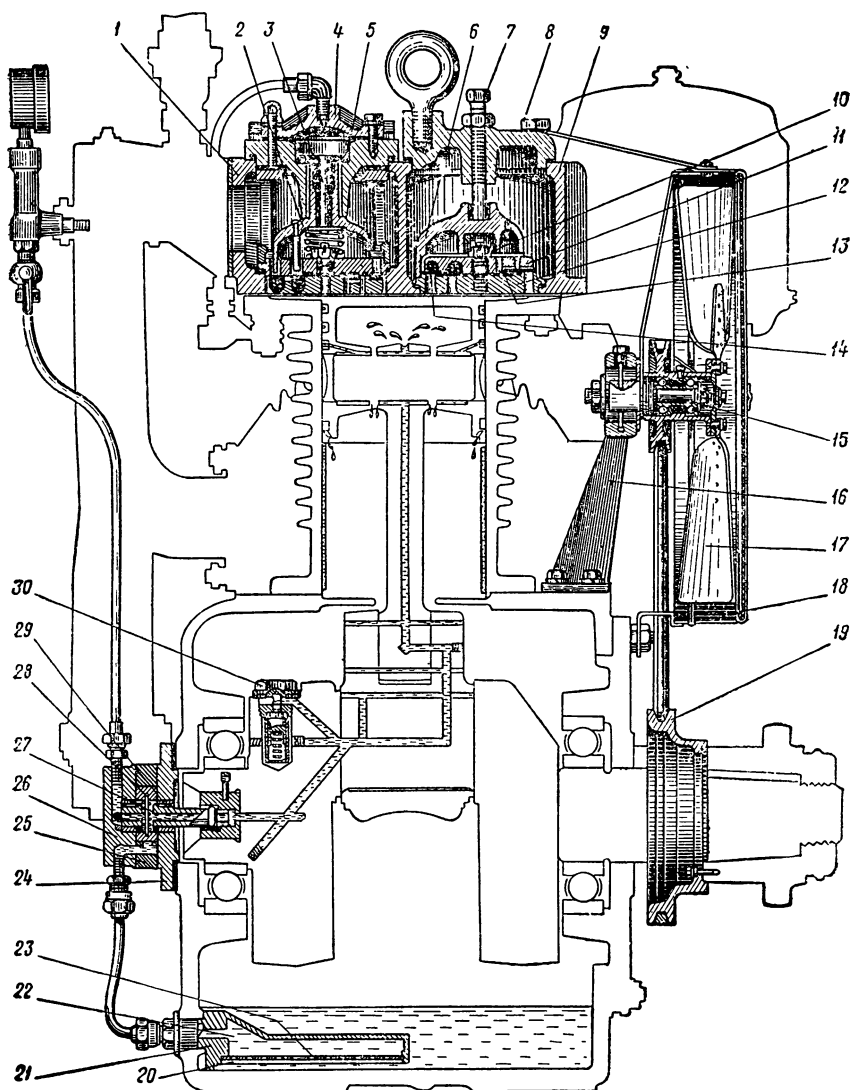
Схема смазки вентилятора и крышка цилиндра компрессора КТ6:
